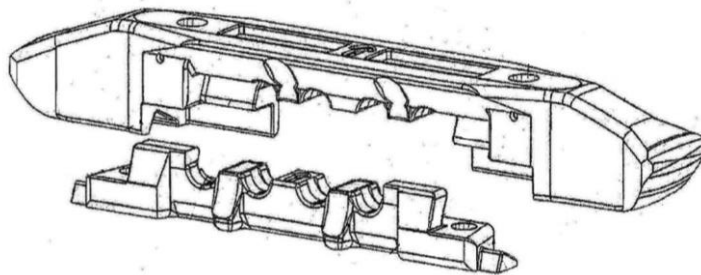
Вид скребка в корисній моделі [6]
